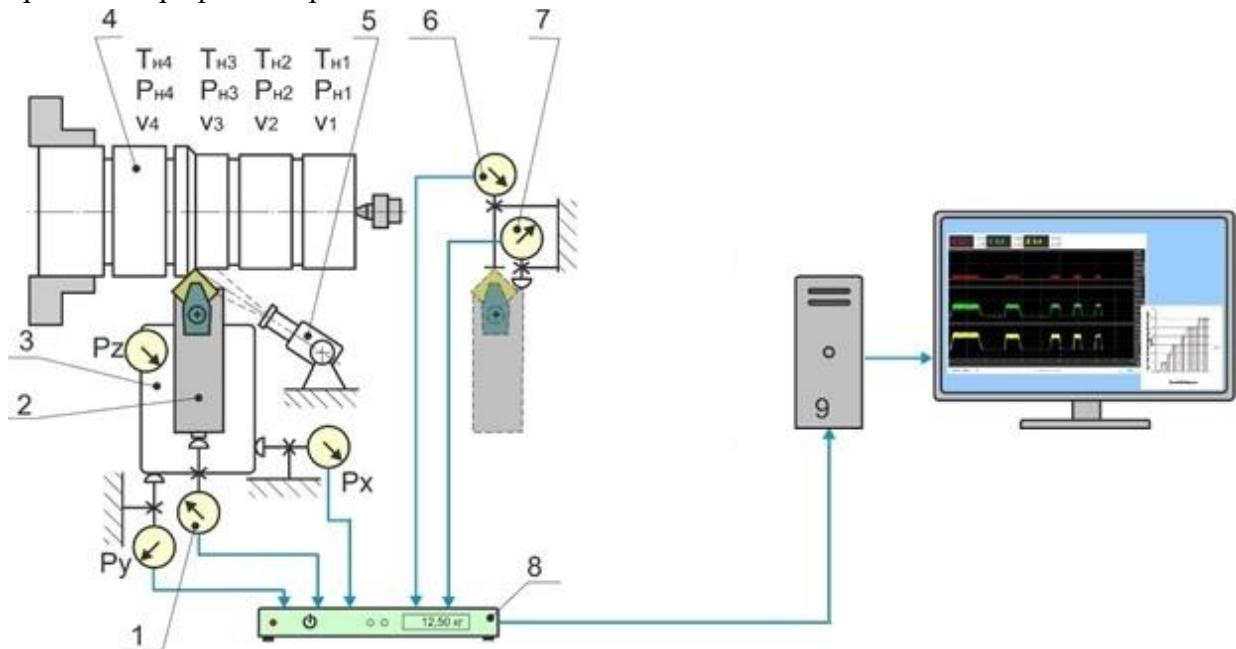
Многопараметрический стенд для обработки образцов деталей.
